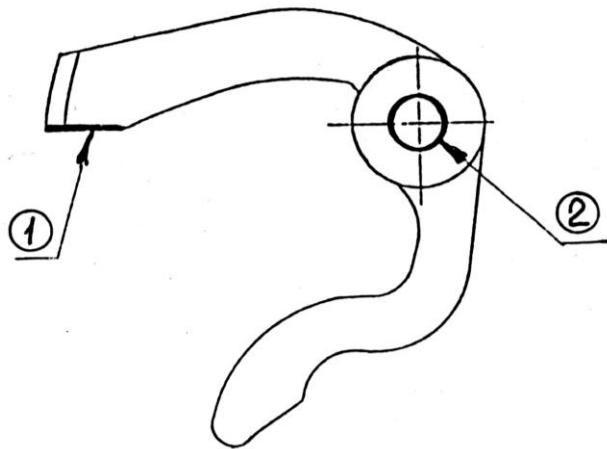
Поверхности износа предохранителя замка автосцепки
